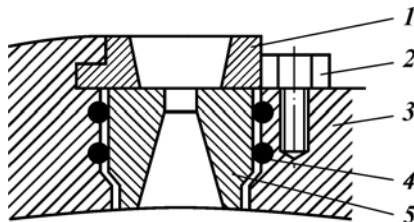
Вариант крепления гидромониторного узла Азинмаша
